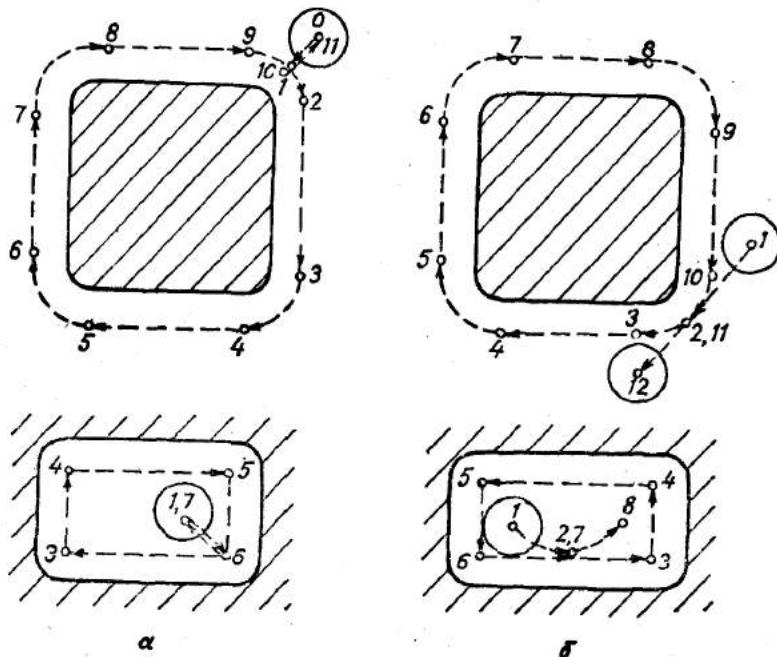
Схеми чорнової (а) та чистової (б) обробки контуру.
